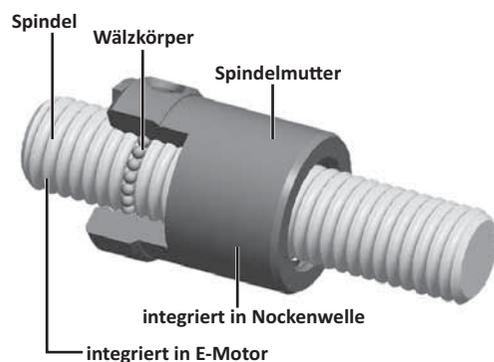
Axialversteller des 3Cam-HX Ventiltriebs
